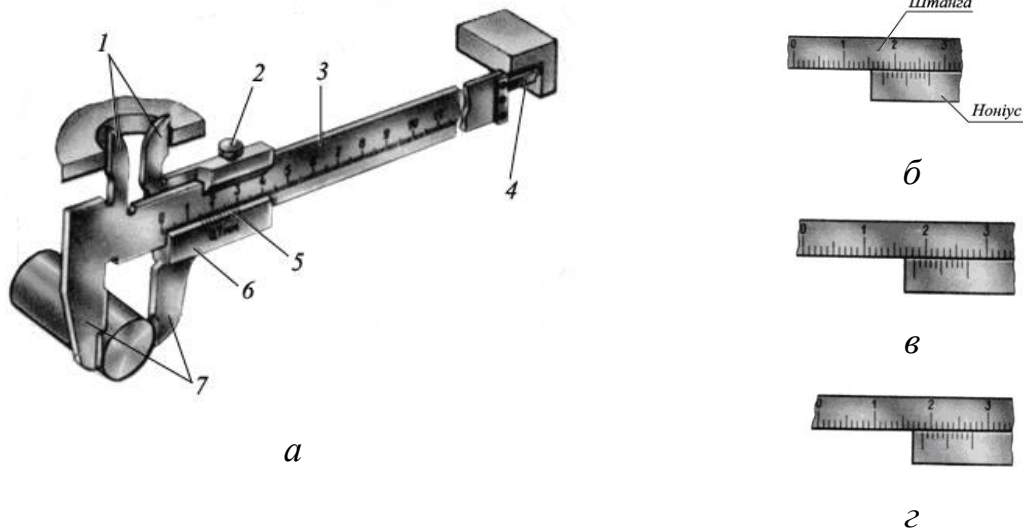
Приклад вимірювання деталей за допомогою штангенциркулю: а — вимірювання елементів деталей штангенциркулем ШЦ-1; б — розмір вимірювальної величини 18 мм; в — розмір вимірювальної величини 18,2 мм; г — розмір вимірювальної величини 18,4 мм; 1 — губки для внутрішніх вимірювань; 2 — затиск; 3 — штанга; 4 — лінійка глибиноміра; 5 — шкала-ноніус; 6 — рамка; 7 — губки для зовнішніх вимірювань
